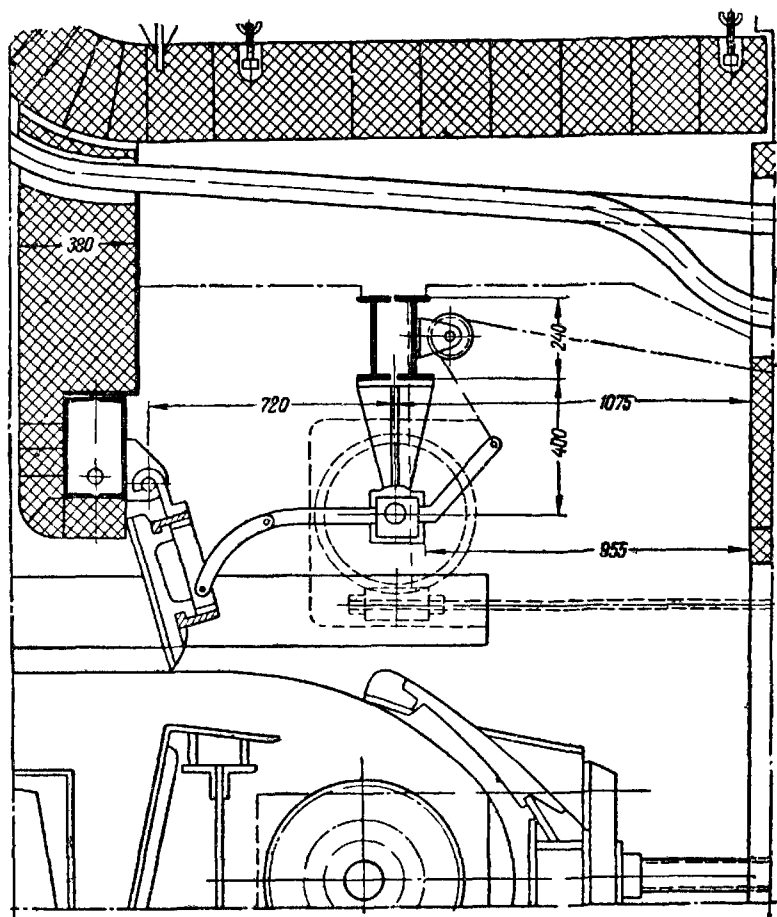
Установка шлакоснимателя и шлакового подпора в топке с цепной решеткой.
